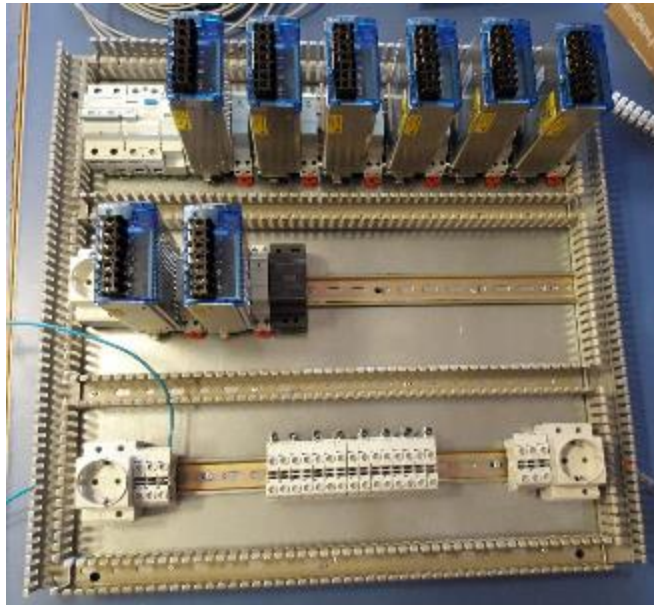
Colocación de carriles DIN sobre la plancha.
